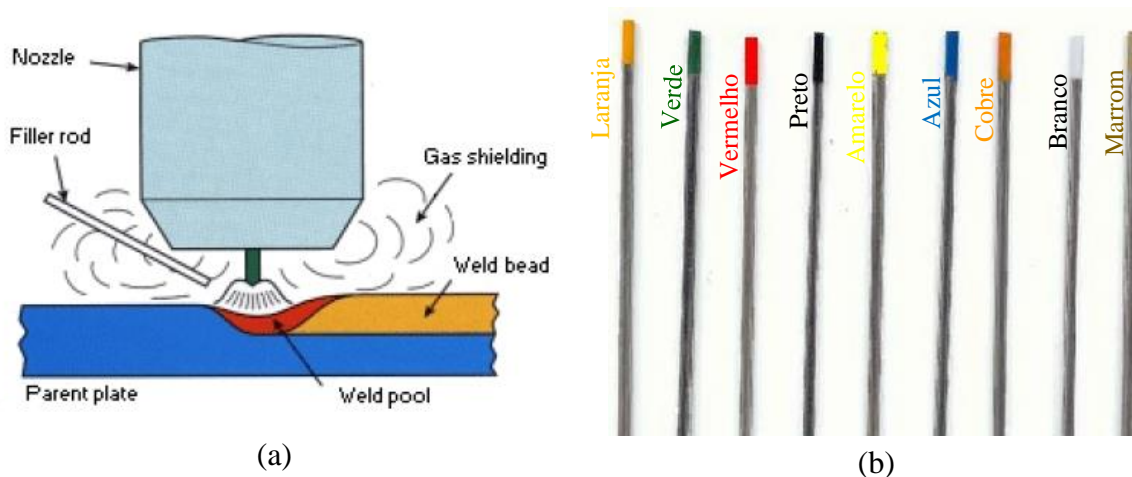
(a) Processo de soldagem a arco elétrico TIG [11]; (b) código de cores para identificação do eletrodo TIG [12].
